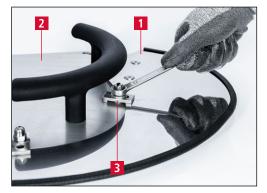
Sichelmesser auf Kopierschleifplatte spannen
